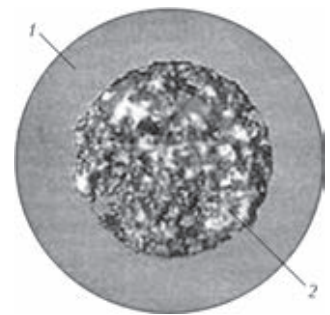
Порошковый присадочный пруток TG-X в разрезе: 1 — оболочка из нержавеющей стали; 2 — флюс
